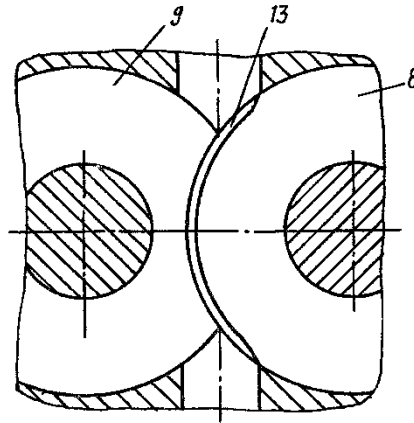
Схема розташування розвантажувальних каналів на циліндричній поверхні підшипників ковзання [67]: 8 і 9 – підшипники ковзання; 13 – розвантажувальні канали.
